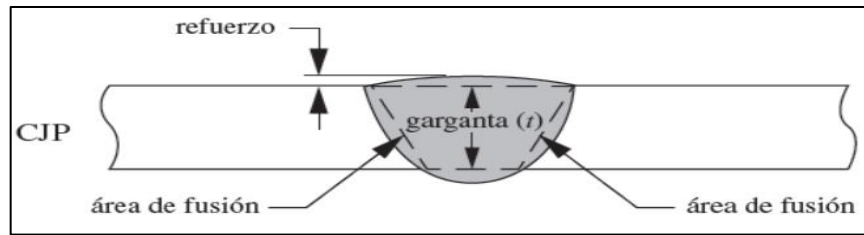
Esfuerzo normal en la soldadura SMAW [42]
